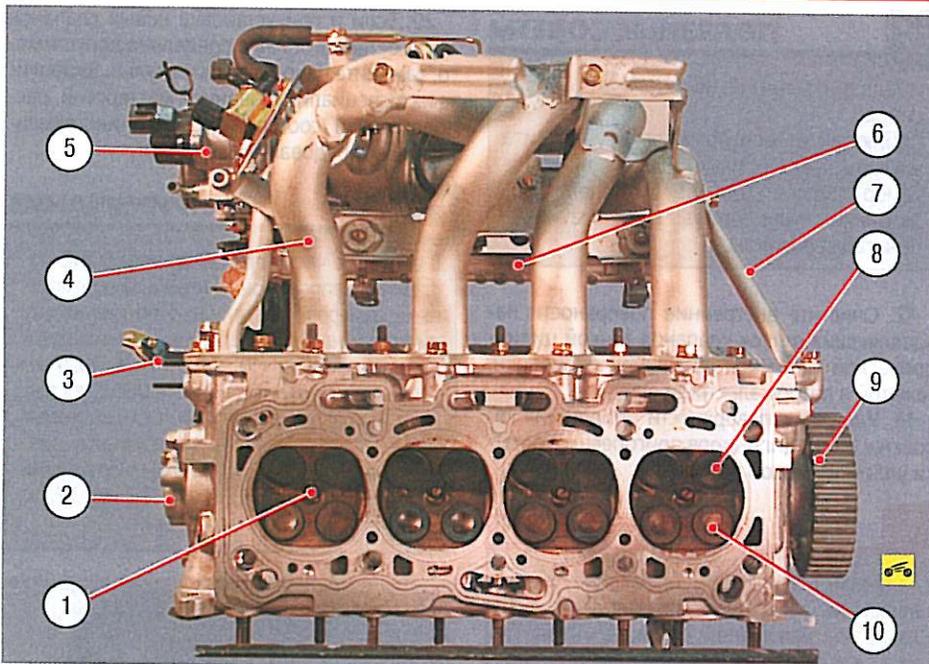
Головка блока цилиндров двигателя SOHC, снятая с автомобиля (вид снизу): 1 – свеча зажигания; 2 – корпус датчика фазы; 3 – поддерживающий кронштейн впускной трубы; 4 – впускная труба; 5 – дроссельный узел; 6 – топливная рампа; 7 – распорка впускной трубы; 8 – впускной клапан; 9 – зубчатый шкив распределительного вала; 10 – выпускной клапан
